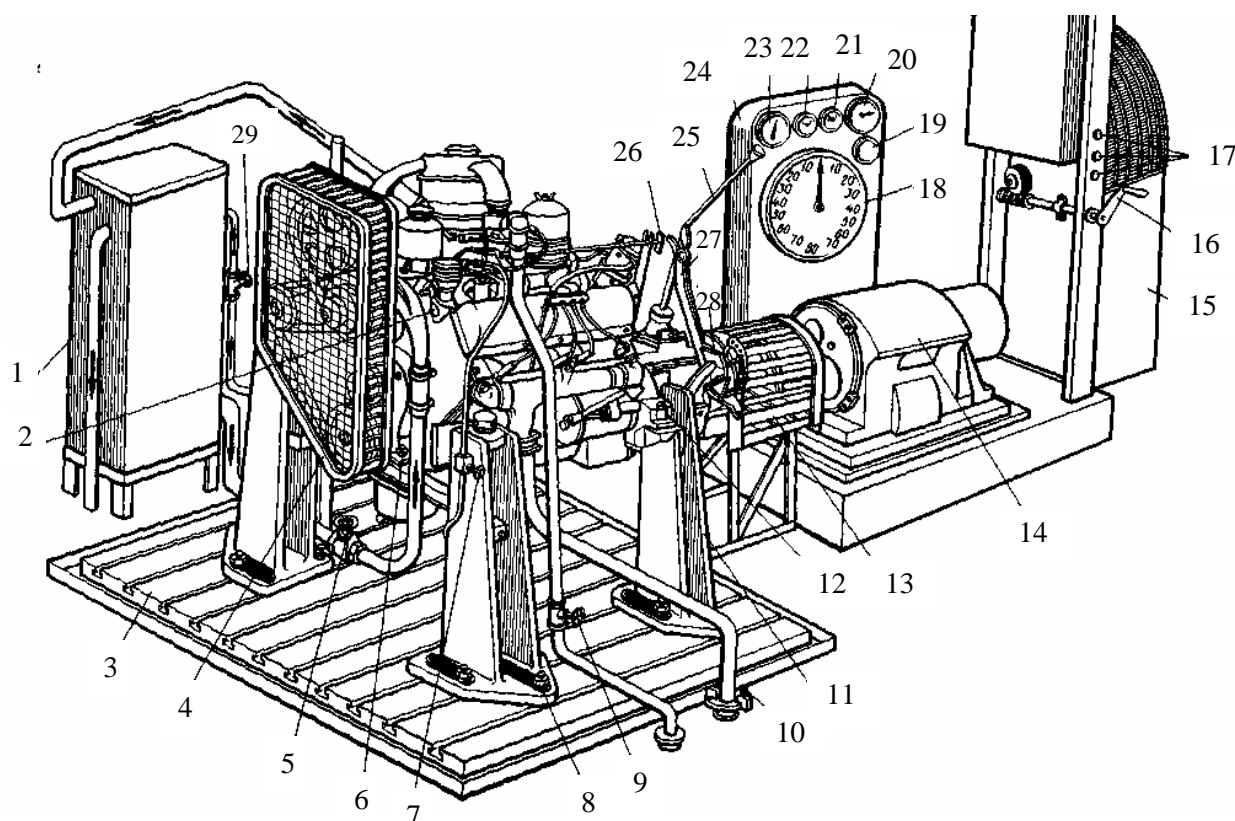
Схема стенда для обкатки и испытания двигателей: 1 – бак; 2 – двигатель; 3 – плита; 4 и 13 – решетки; 5, 9 и 29 – вентили; 6, 8 и 12 – элементы крепления двигателя; 7 – кран; 10 – элементы крепления газоотводной трубы; 11 – стойка; 14 – электромашина; 15 – реостат; 16 – рукоятка управления реостатом; 17 – кнопки; 18 – шкала; 19 – сигнализатор; 20 – тахометр; 21 и 22 – термометры; 23 – манометр; 24 – корпус; 25 – рычаг коробки передач; 26 – тяга; 27 – рычаг ручного тормоза; 28 – педаль
